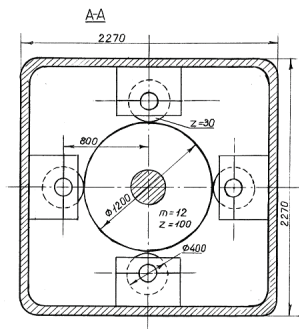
Привод вертикальной клетки прокатного стана. Редуктор.
